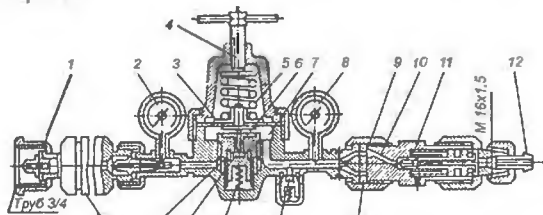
Схема газового редуктора У-30 для вуглекислого газу:
